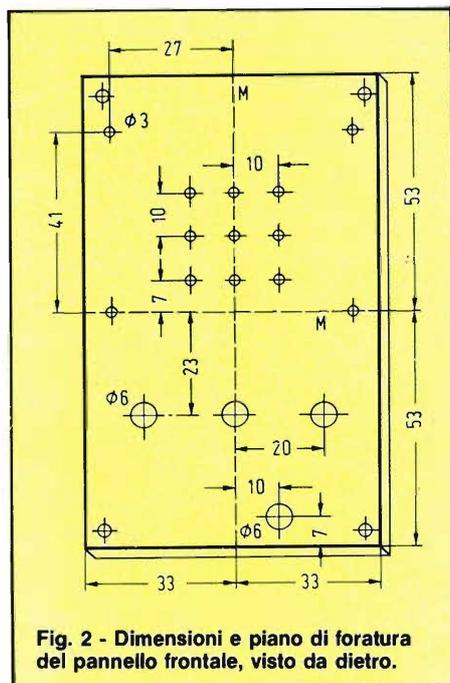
Dimensioni e piano di foratura del pannello frontale, visto da dietro.
